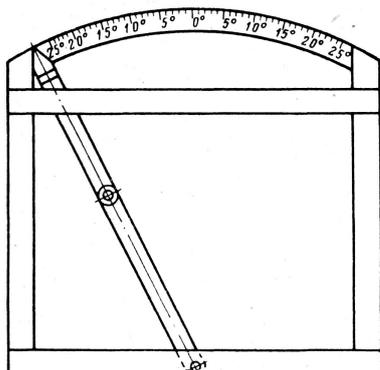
Угломер для определения угла перекоса петельных столбиков и
